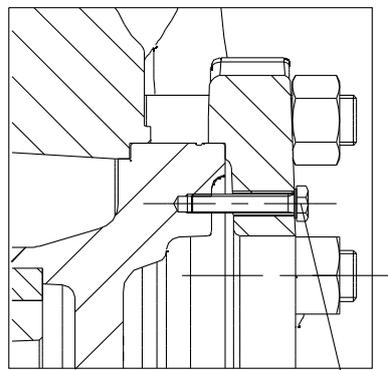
Чертеж общего вида — стандартное исполнение (со смазкой маслом)
